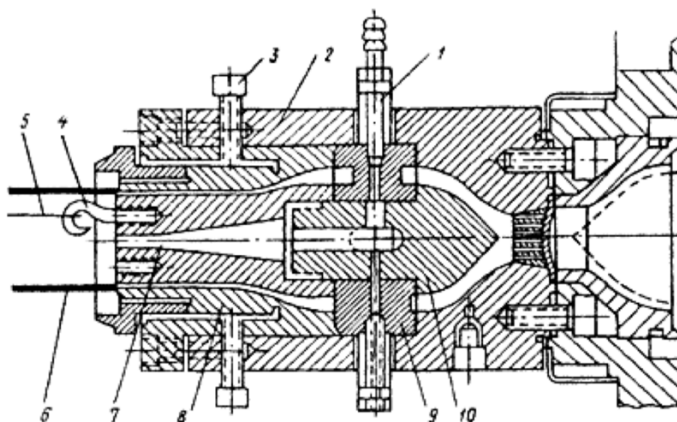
Прямоточна кільцева головка для виготовлення труб і шлангів:
